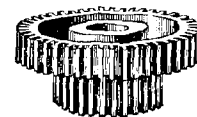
Engrenages droits de l'arbre porte-volant.
